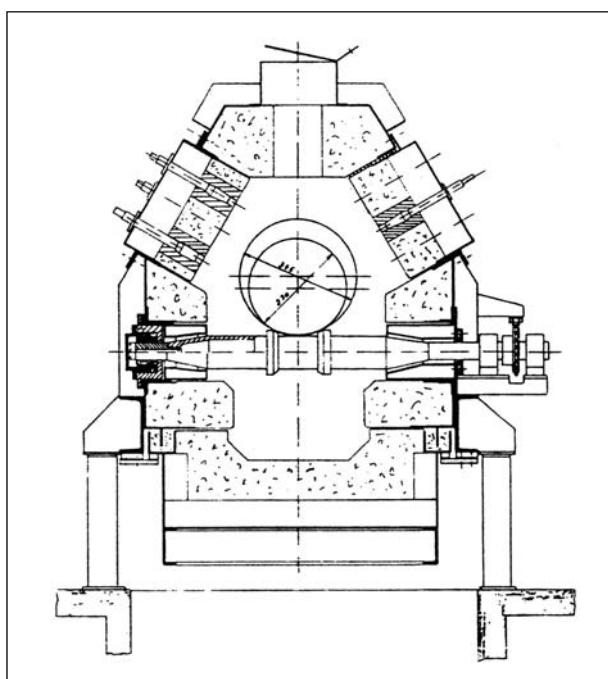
Роликовая печь DFI скоростного нагрева заготовок из цветных металлов (ФРГ)
